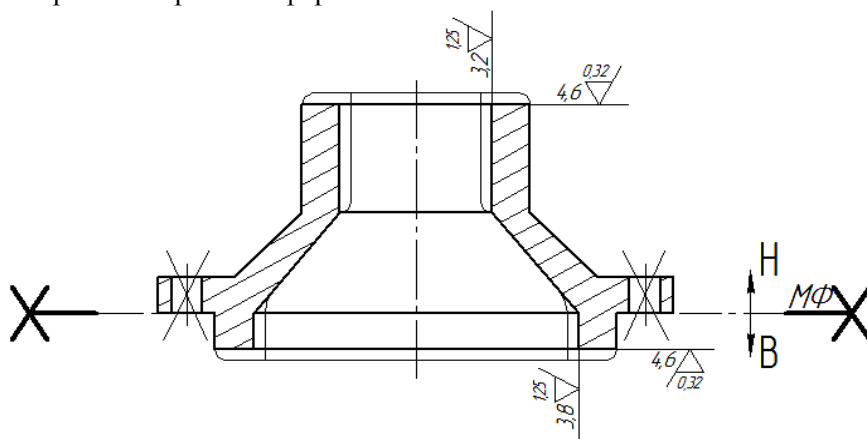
Обозначение разъема модели и формы и положения отливки при заливке
